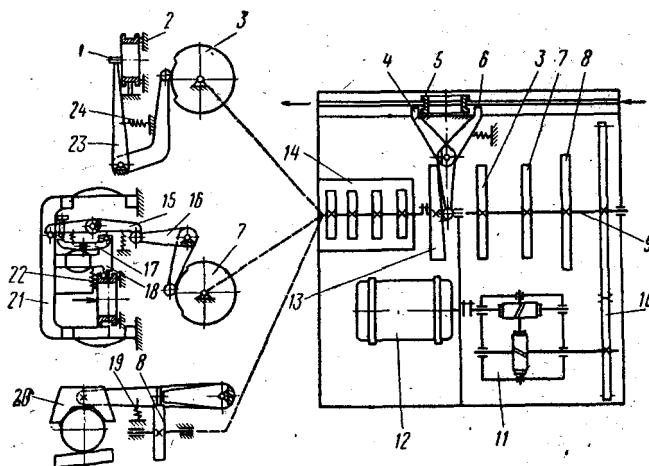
Кинематическая схема устройства ОКБ-1111 для подналадки бесцентрово-шлифовального станка
